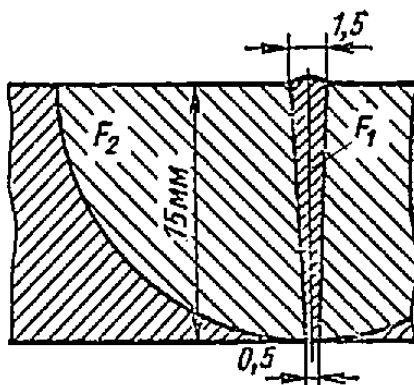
Проплавление при электронно-лучевой и электродуговой сварке:  $F_1$  – сечение шва при электронно-лучевой сварке;  $F_2$  – сечение шва при ручной дуговой сварке
